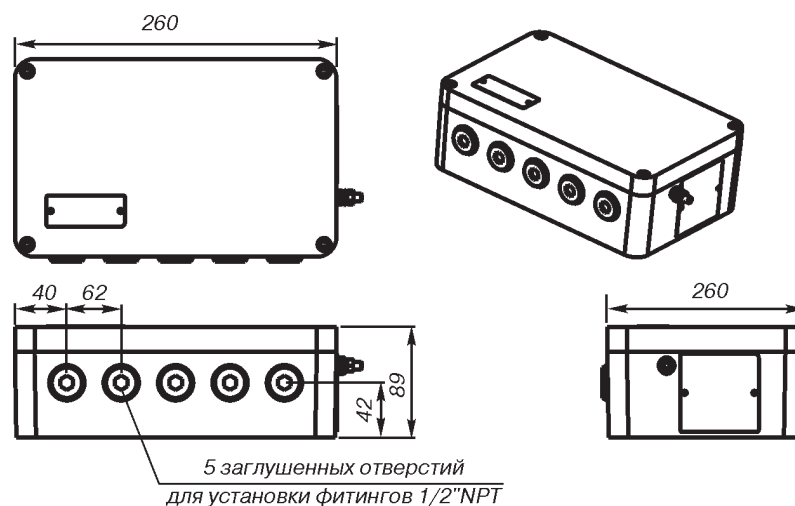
Дополнительная соединительная коробка из алюминия/пластика (ввод кабелепровода, код опций JA3 и JP3).
